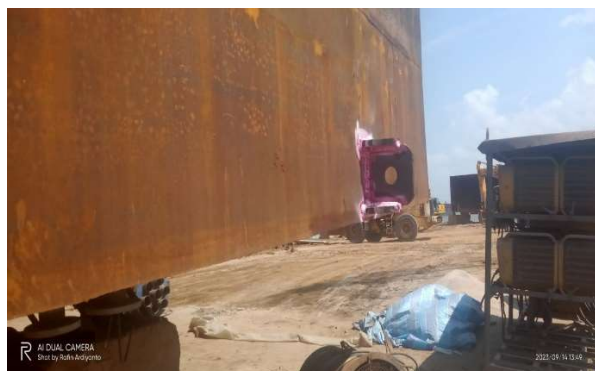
Penetran test kupingan blok frame 0-29 T.033 Louis Dolphin
